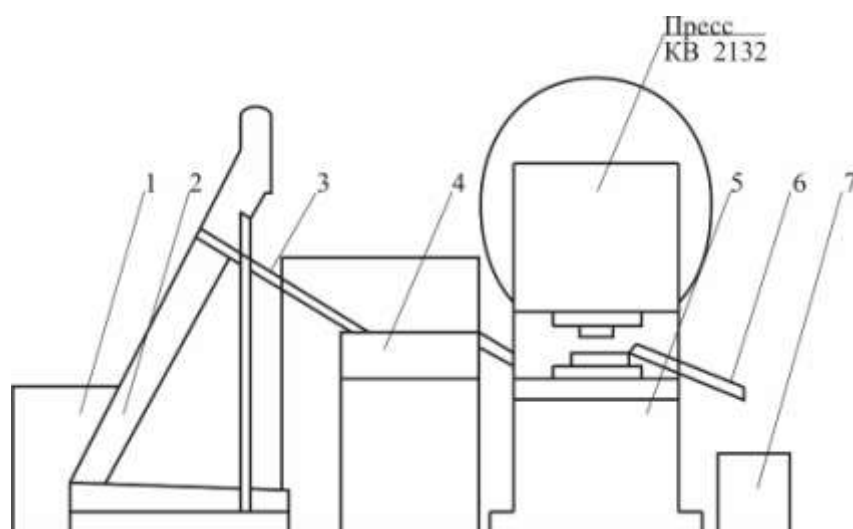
Участок автоматической линии штамповки корпуса форсунки
